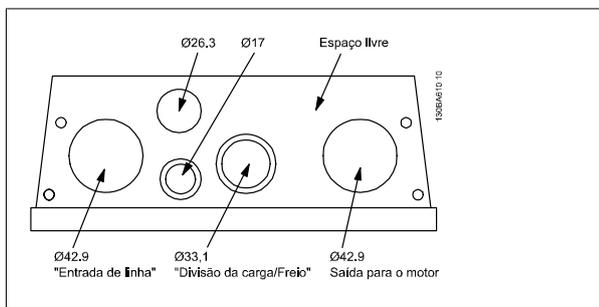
Furos para entrada do cabo do gabinete metálico B2. As sugestões de uso dos furos compreendem apenas recomendações; outras soluções são possíveis.
